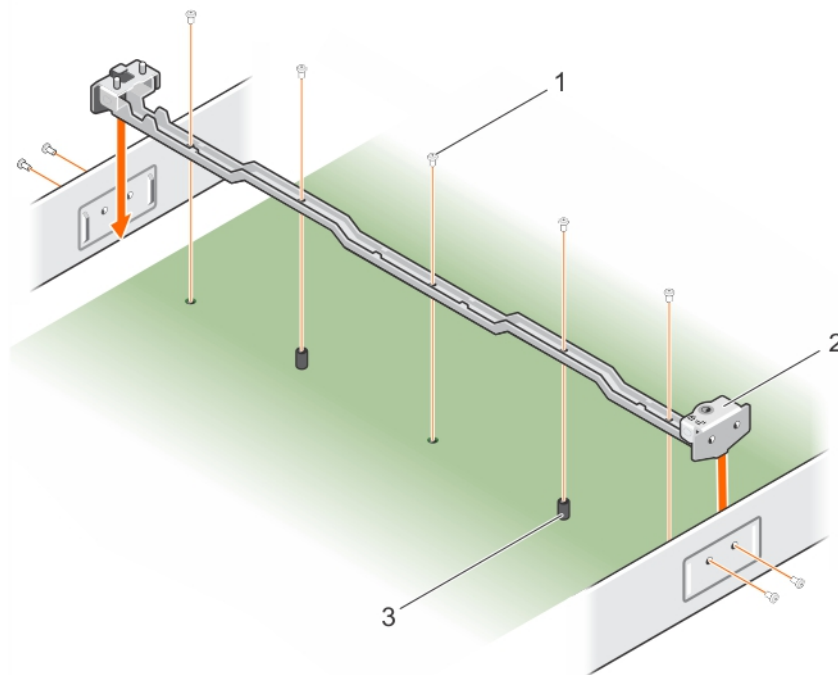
Instalación de la barra de retención de la cubierta de enfriamiento
